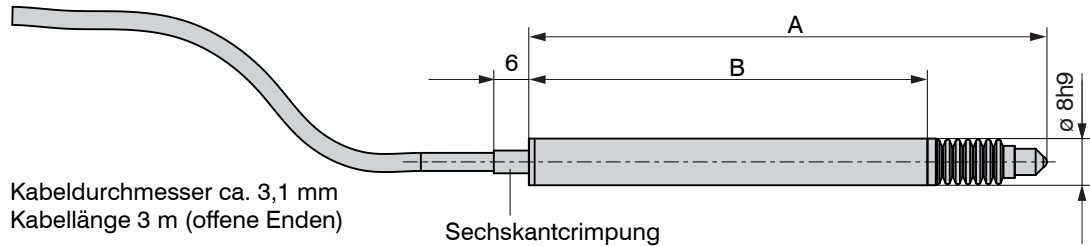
Gehäusemaße für Messtaster DTA-xG8-3-CA
